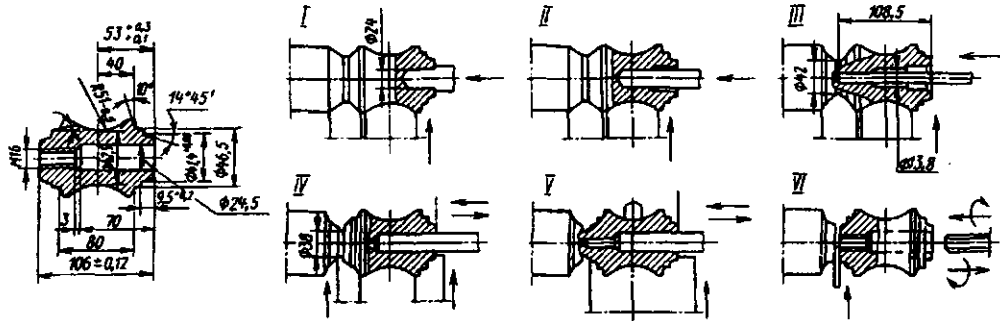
Наладка шестишпиндельного автомата для обработки червяка
